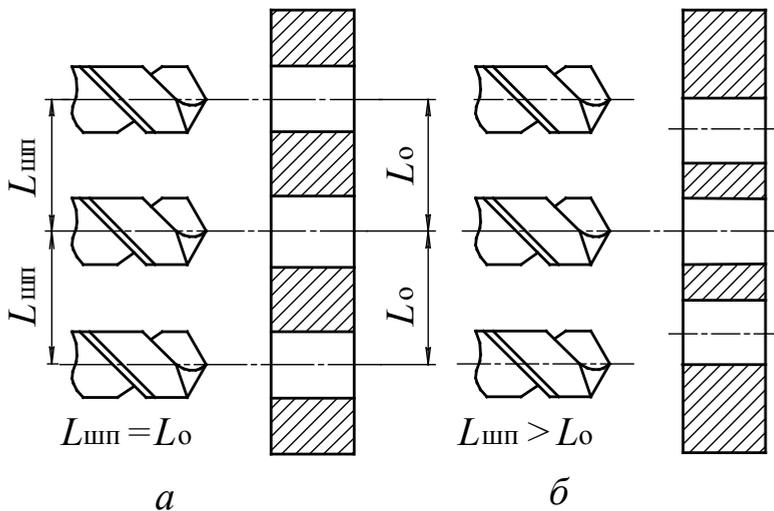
Конструкция корпусных деталей с отверстиями:
